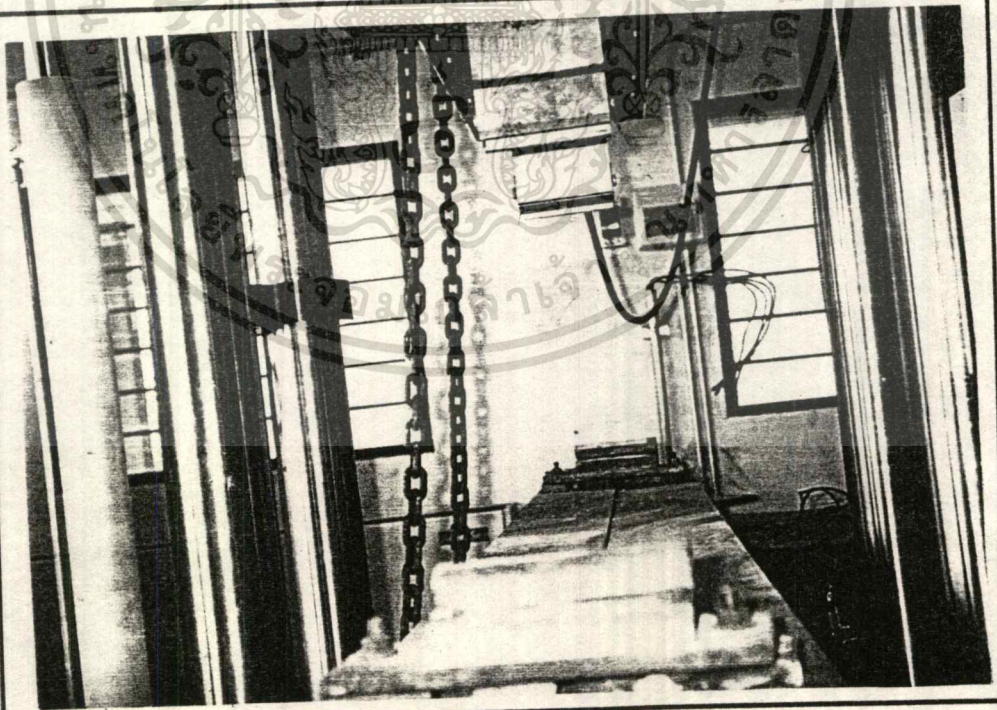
แสดงการขึ้นรูป Steel Welded Wire Mesh โดยเครื่องตัดเหล็ก
